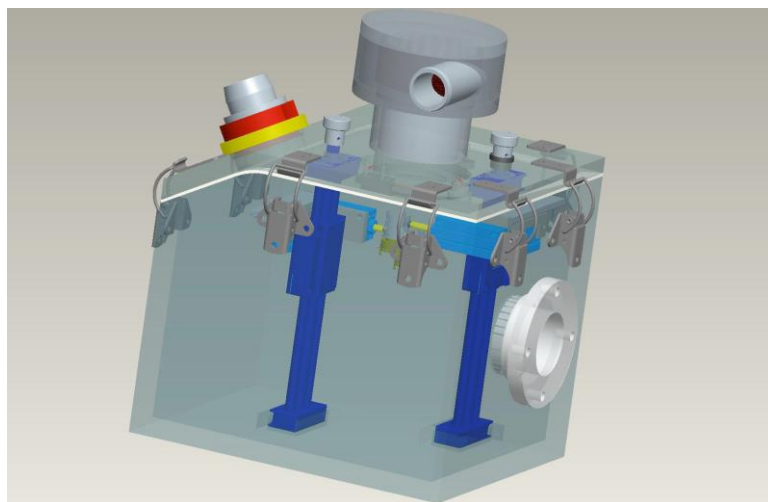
Disegno del banco prova nel suo insieme realizzato in Pro|Engineer.
